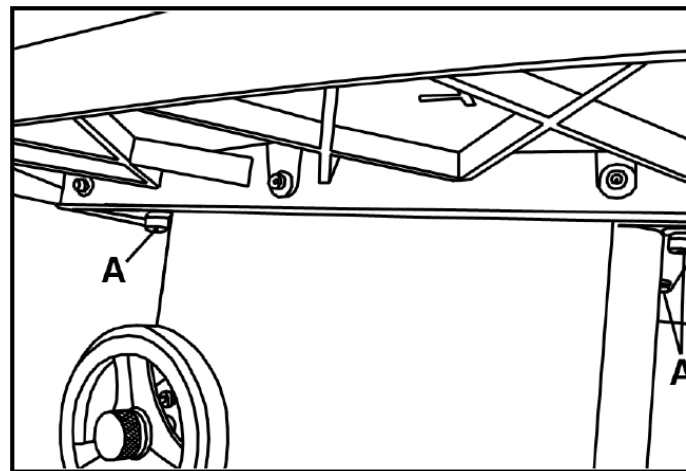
Регулировка цапф для юстировки диска и пазы под угловой упор
